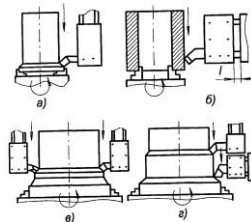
Схемы обработки на токарно-карусельных станках
